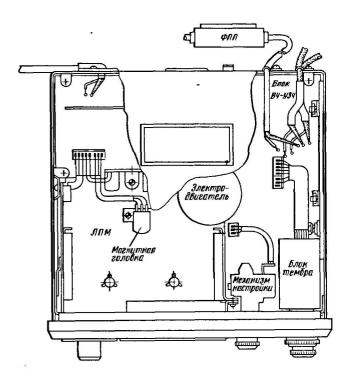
Схема расположения осиовных узлов и деталей в корпусе автомагнитолы «Былииа РМ-317CA» (вид сверху)
